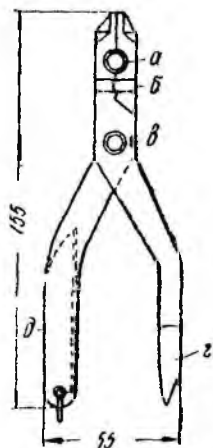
Универсальные щипцы-обжим: а — обжим; б — резец для резки шнура; в — резец для резки провода; — медный наконечник; д — нож.
